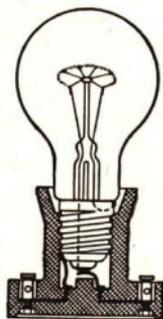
/2. Berührungssichere Lampenfassung einer Glühlampe (Schnittzeichnung, schematisch)
